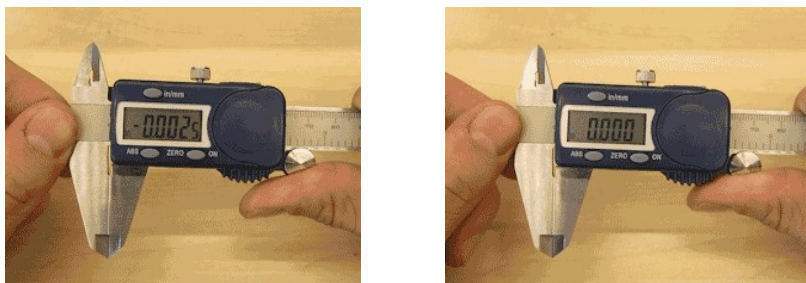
Обнуление цифровой шкалы штангенциркуля
